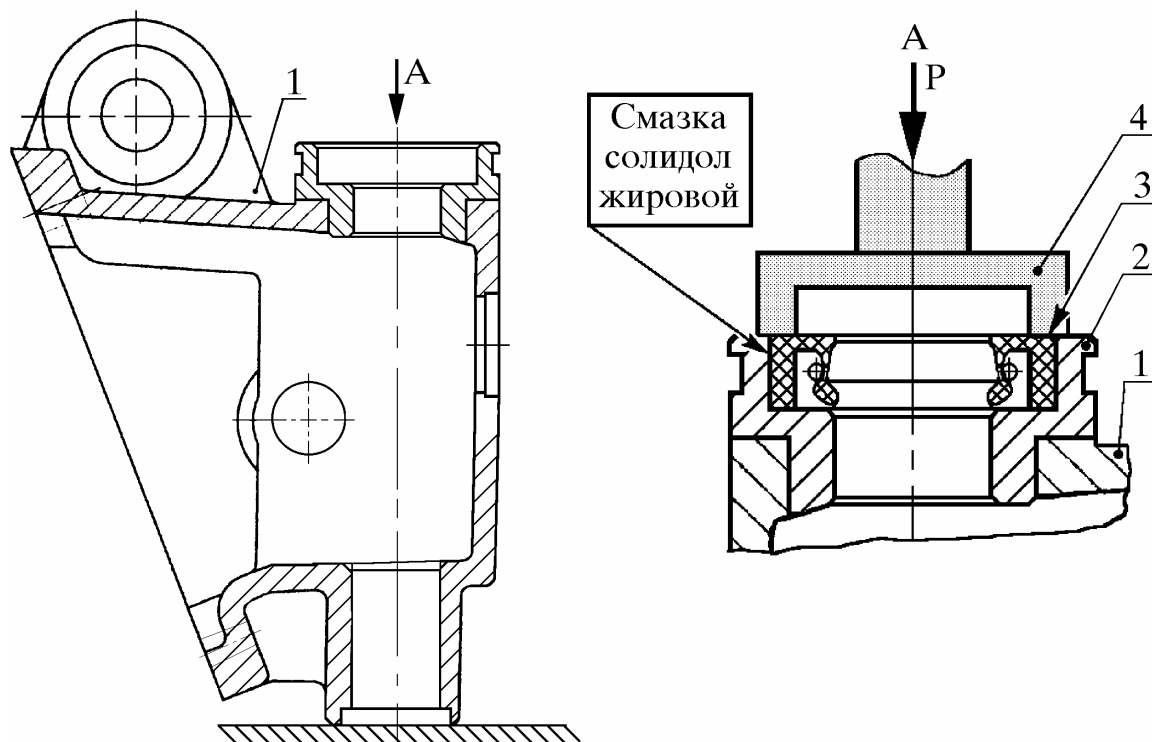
Запрессовка манжеты в отверстие втулки корпуса механизма переключения передач:
